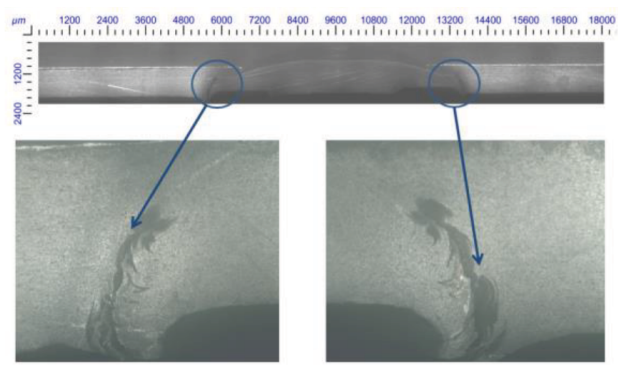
Микроструктура сварного соединения образца № 3 с непроваром по кромке сварного соединения.
